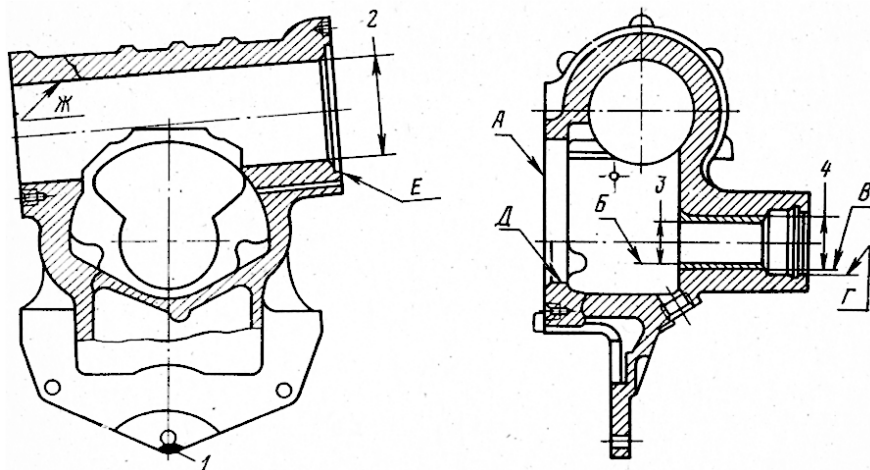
Картер рулевого механизма автомобиля ЗИЛ
